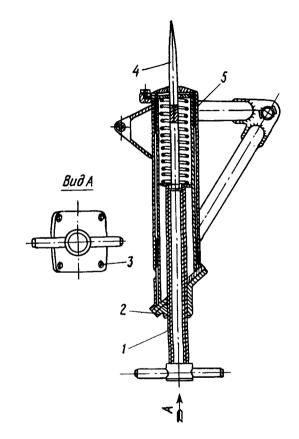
Приспособление для сборки шкворня с фермой: I — винт нажимной; 2 — гайка фланцевая; 3 — болт; 4 — наконечник направляющий; 5 — ферма хвостовой опоры Ш4200-0
